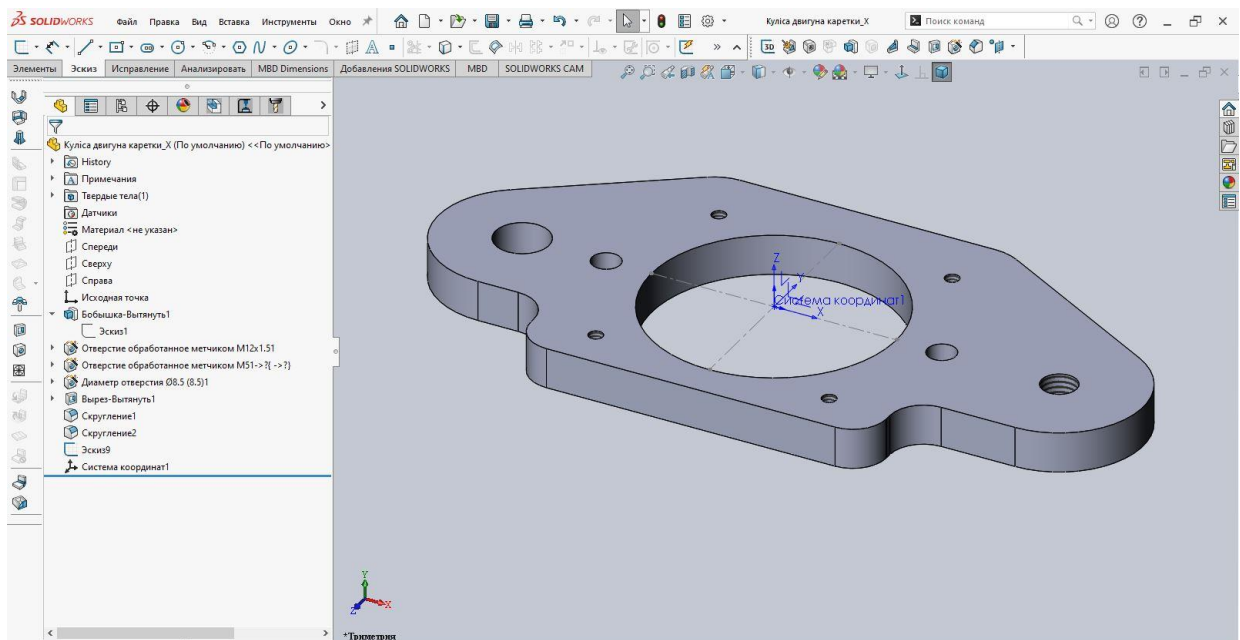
3D модель деталі «Куліса двигуна катерки Y»
